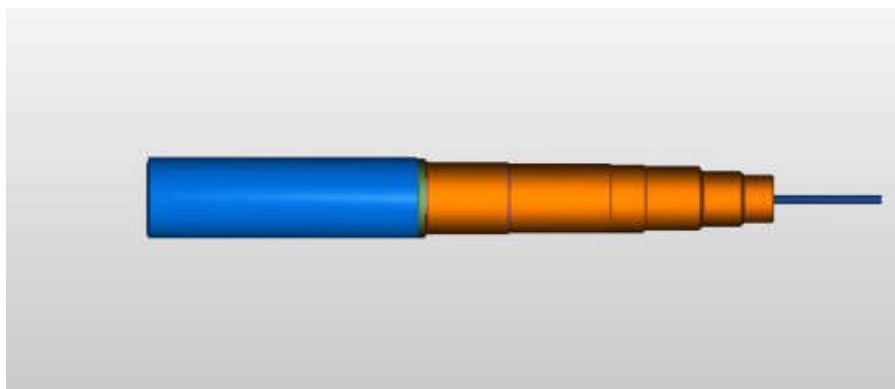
Візуалізація чорнової обробки поверхні $\varnothing 62^{+0,74}$
